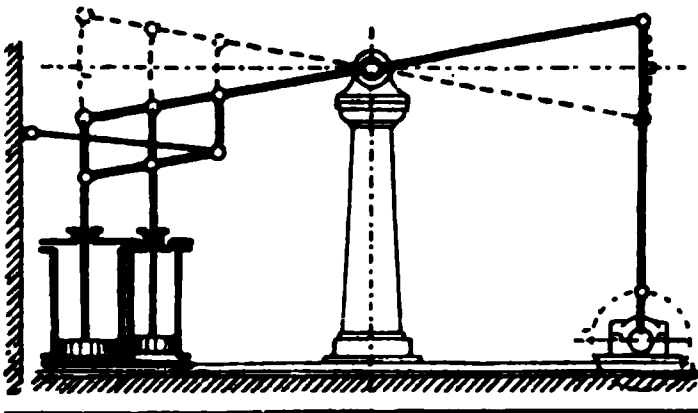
Woolfsche Balanciermaschine mit gleichgerichtetem Kolbenlauf, wird noch jetzt für Pumpmaschinen etc. ausgeführt.
